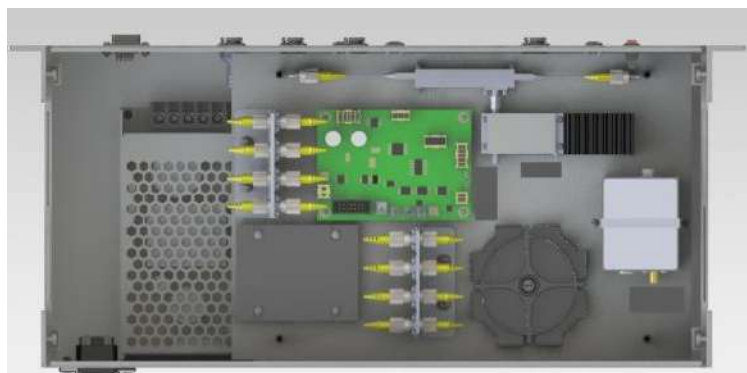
Установка для измерения хроматической дисперсии без крышки: вид сверху
